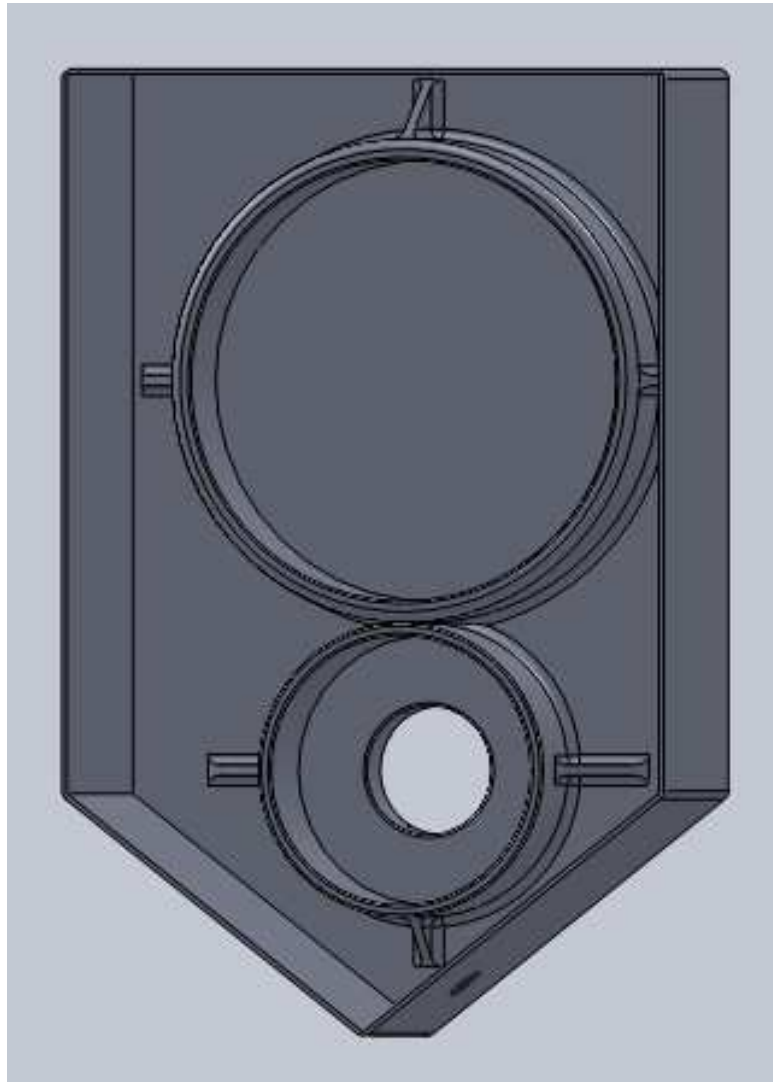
Prototipo carter lato motore con cuscinetti interni
